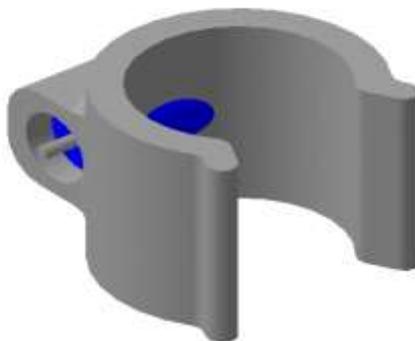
Пластмассовый корпус, крепления и датчик
